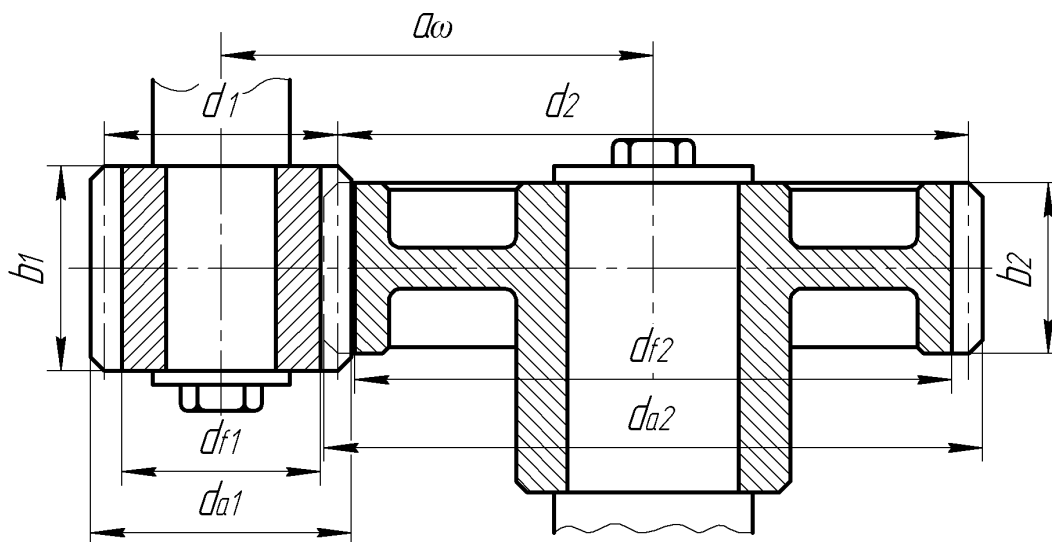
Основные геометрические параметры открытой цилиндрической зубчатой передачи
